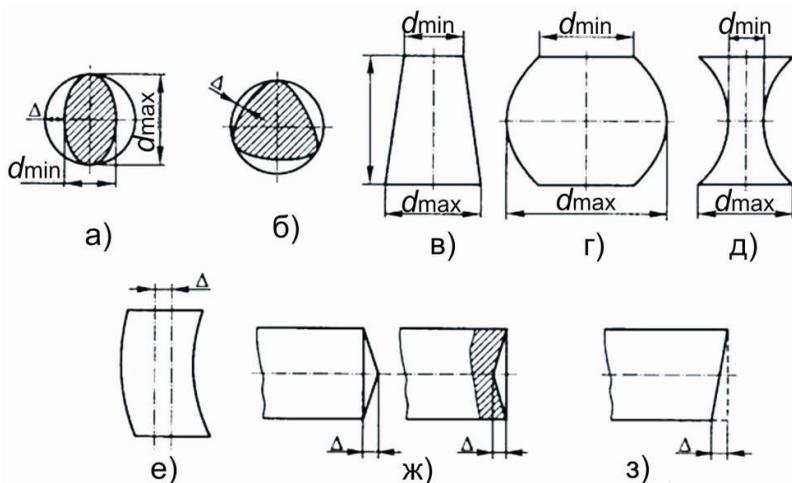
Основные виды дефектов наружных цилиндрических и торцовых поверхностей:
